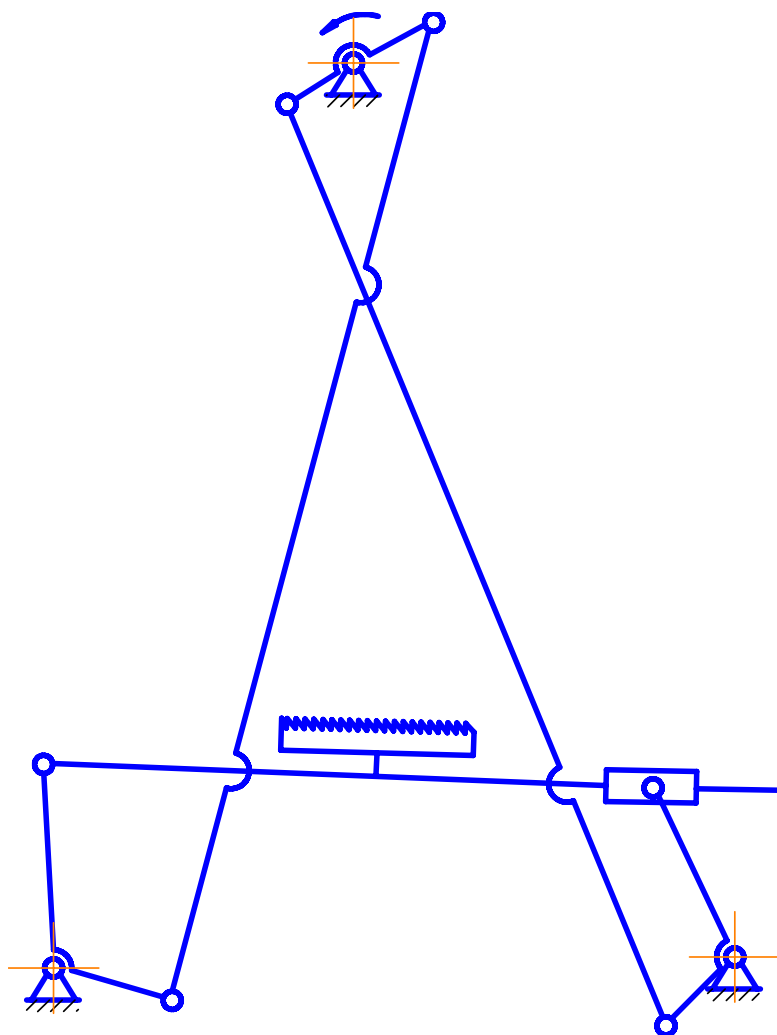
Механизм перемещения материала стачивающей машины 2222 класса однониточного цепного стежка
